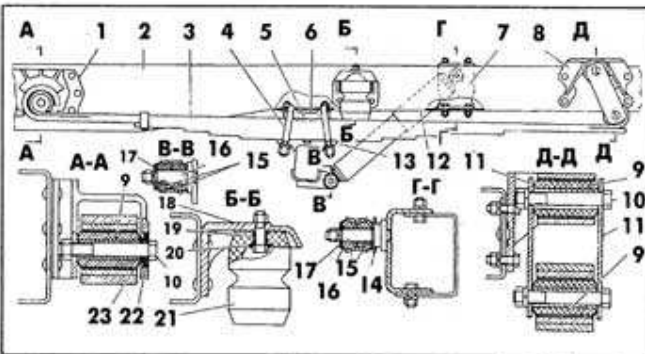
Задняя подвеска автобусов типа 4x2: 1, 7, 8 и 18 – кронштейны; 2 – лонжерон рамы; 3 – рессора; 4 – стремянка; 5 – на-кладка; 6 – буфер; 9 – резинометаллические шарниры; 10 – болт; 11 – серьга; 12 – амортизатор; 13 – подушка рессоры; 14, 17, 20 и 23 – шайбы; 15 – резиновые втулки; 16 – палец; 19 – втулка распорная; 21 – резиновая рессора сжатия; 22 – шайба тарельчатая.
